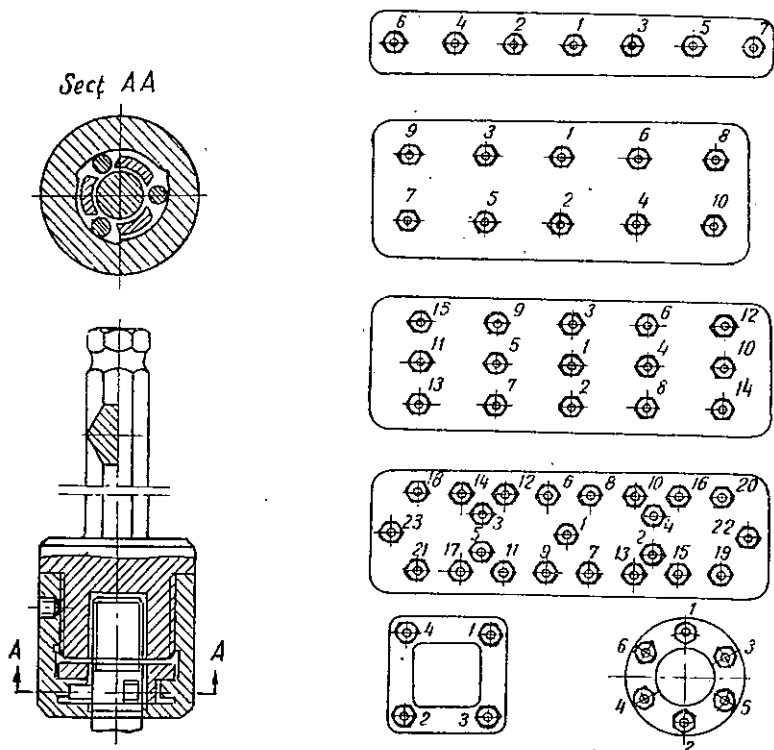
Mandrină cu role pentru înșurubarea mecanizată a prezoanelor
